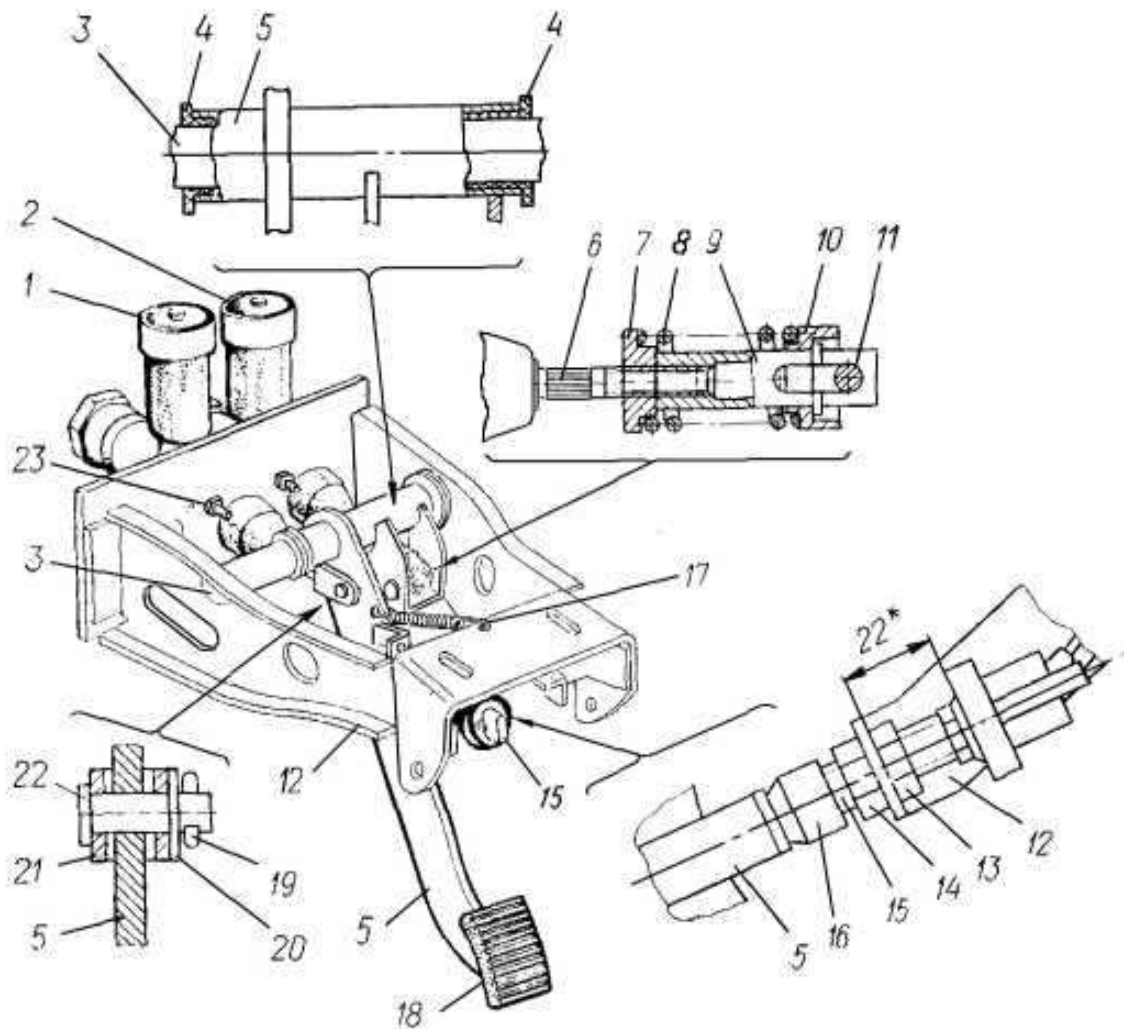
Главные тормозные цилиндры, педаль тормоза и выключатель сигнала торможения: 1 — главный тормозной цилиндр контура гидропривода тормозов передних колёс; 2 — главный тормозной цилиндр контура гидропривода тормозов задних колёс; 3 — ось педалей; 4 — втулка педали; 5 — педаль тормоза в сборе; 6 — толкатель главного тормозного цилиндра; 7 — гайка специальная; 8 — пружина (регулятор тормозных сил); 9 — шток; 10 — шайба опорная; 11, 22 — палец; 12 — кронштейн педалей; 13 — контргайка; 14 — гайка (приварная); 15 — выключатель сигнала торможения (ВК412); 16 — наконечник выключателя; 17 — пружина педали оттяжная; 18 — накладка; 19 — шплинт; 20 — шайба; 21 — вилка толкателя; 23 — гайка крепления цилиндра; * номинальный размер установки выключателя, при котором в верхнем крайнем положении педали контакты выключателя разомкнуты. В случае их неразмыкания допускается некоторое уменьшение размера — ввинчивание выключателя в гайку 14 до получения надёжного размыкания.
